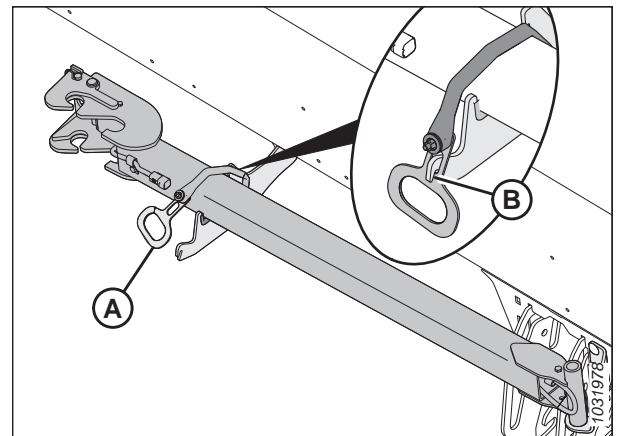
Almacenamiento de la extensión de la barra de remolque
